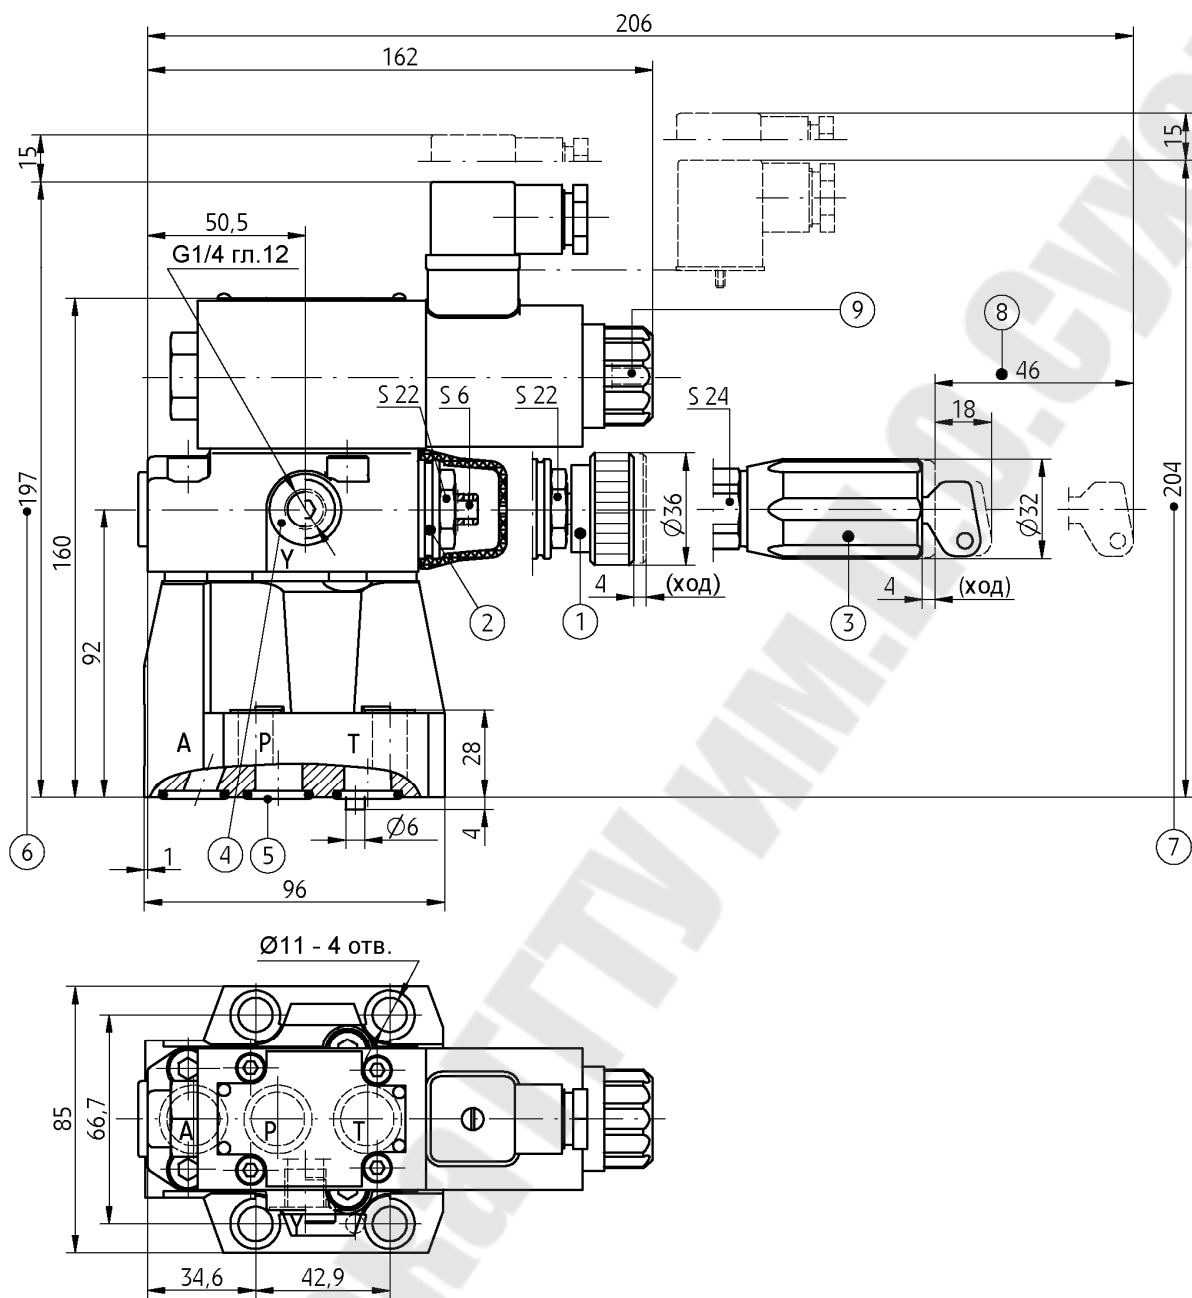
Общий вид и габаритные размеры разгрузочного клапана непрямого действия типа UZ0PW10-A2-52/50-10G24 NZ4
